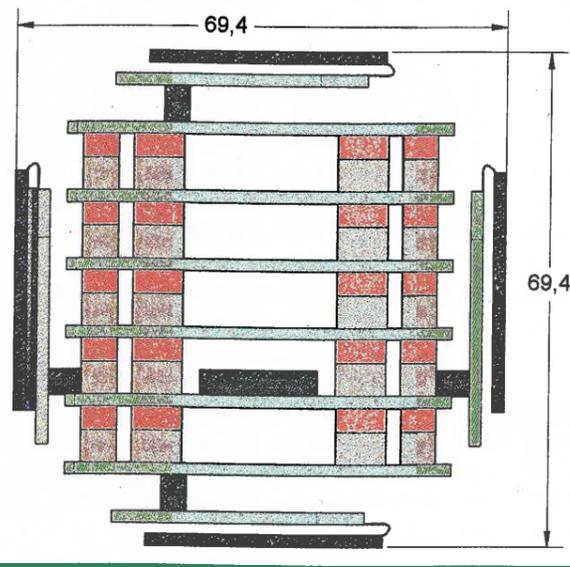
Prinzipieller mechanischer Aufbau des Würfels (Abmessungen in Millimeter)
